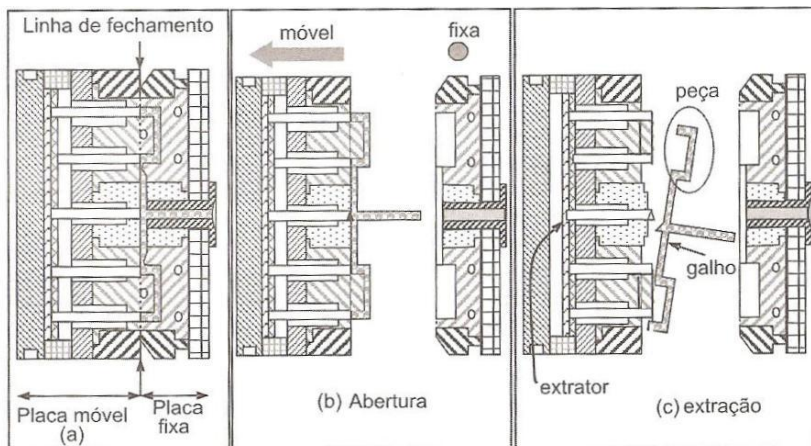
Molde de duas placas: (a) molde fechado, (b) molde abrindo e (c) molde acionado o sistema de extração e a peça caindo. Fonte: MANRICH, 2005, p. 362.
